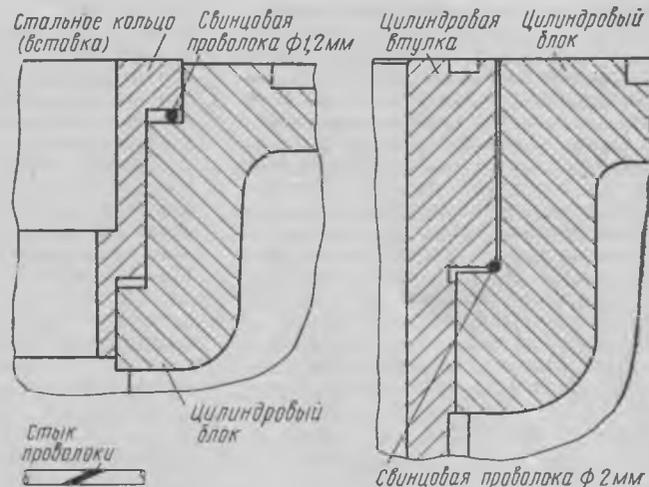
Укладка свинцовой проволоки в блок дизеля Д50 под стальные кольца цилиндрических блоков (слева) и под бурт цилиндрической втулки (справа)
